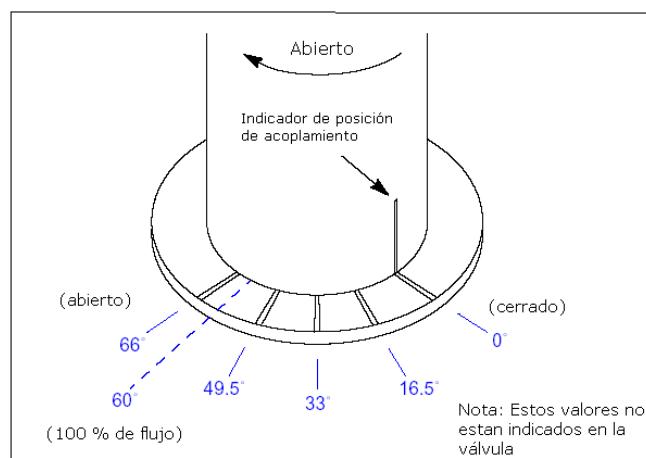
Indicador de posición (Fuente: Rotary fuel valve and position controller for gas turbines)
